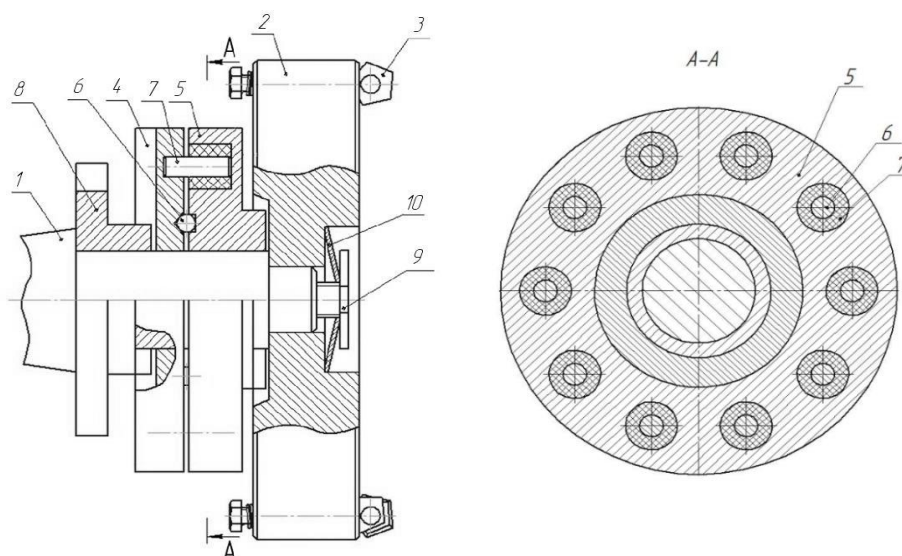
Сборная торцовая фреза с демпфирующими элементами:
